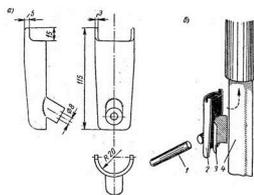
Приспособление для затяжки гайки-сальника пера передней вилки:
